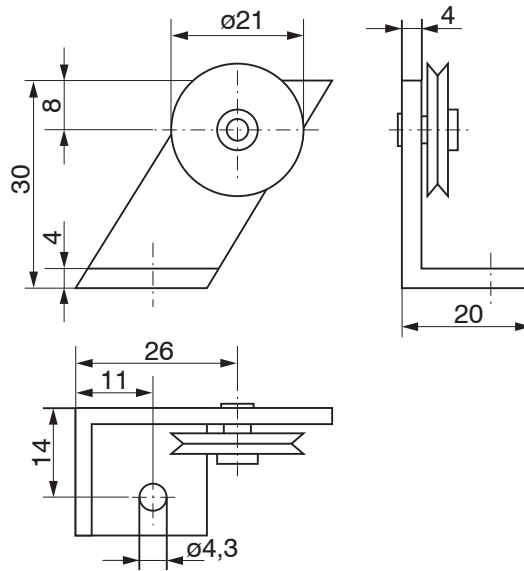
Umlenkrolle TR3-WDS, fest, mit Montagefuß, Abmessungen in mm
